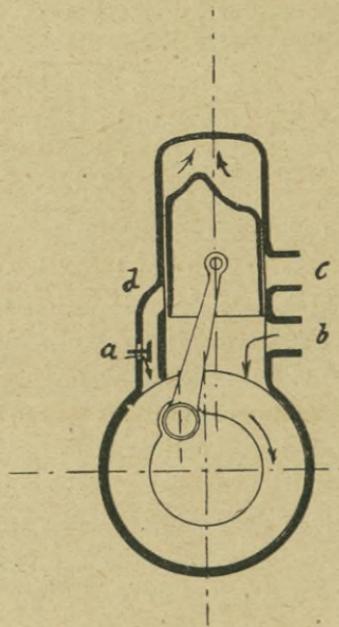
Zweitaktmotor mit selbsttätigem Einlaßventil (Verdichtung des Gasgemisches).
